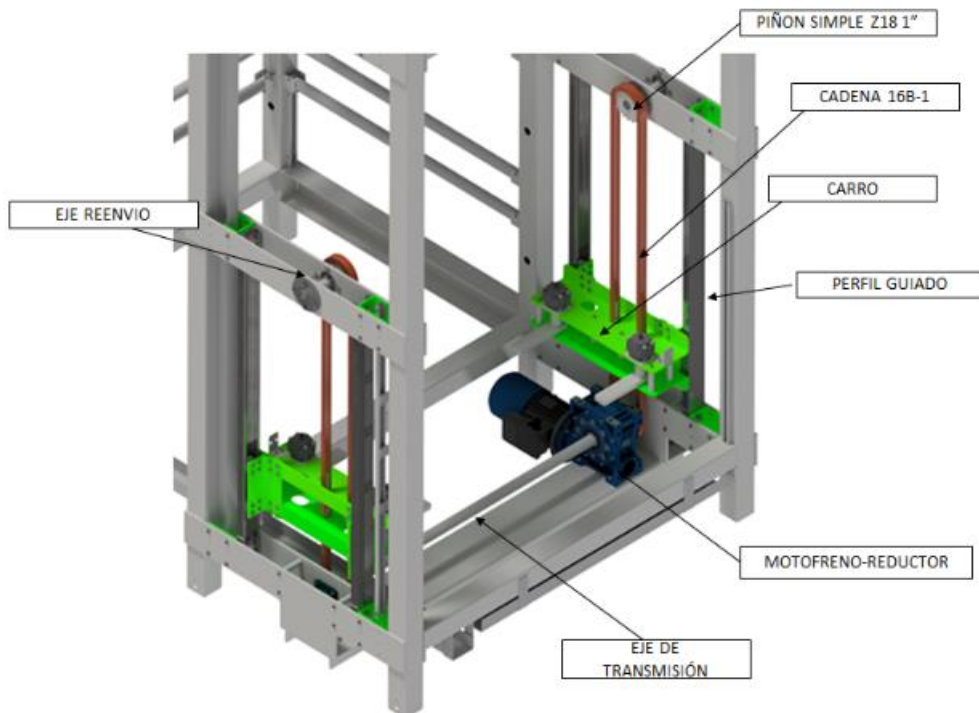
Módulo desapilado (sistema elevación contenedores)
